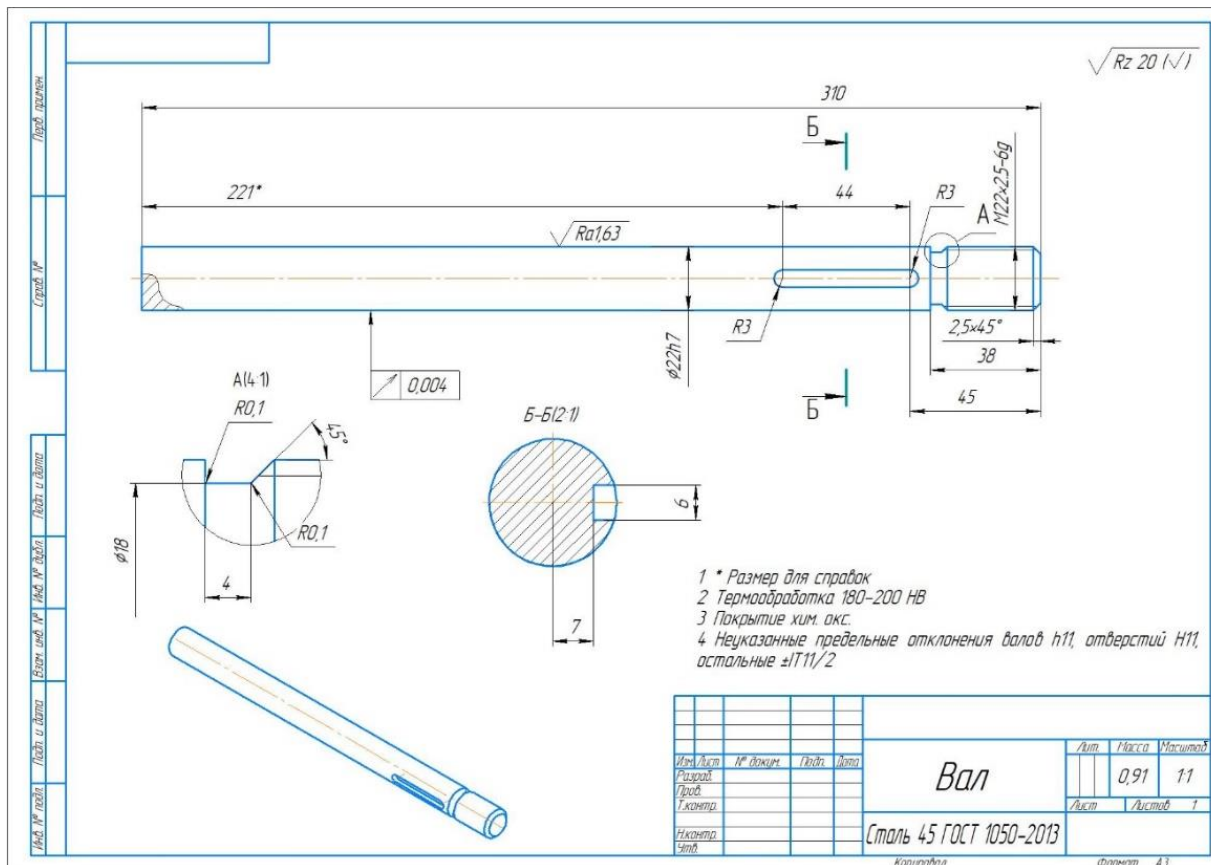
Рабочий чертеж детали вал, выполненный по модели
